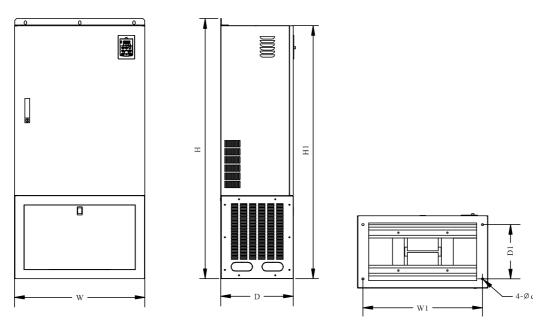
Внешний вид инвертора SL9 шкафного исполнения
